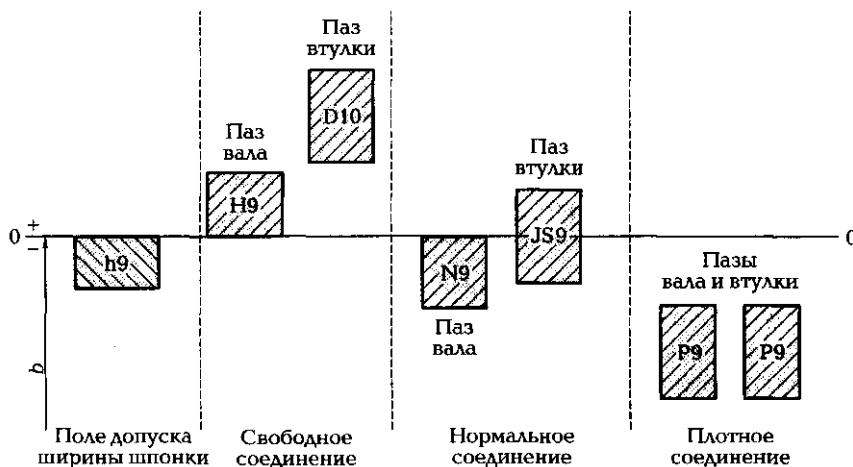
Схема расположения полей допусков по ширине шпонки:
